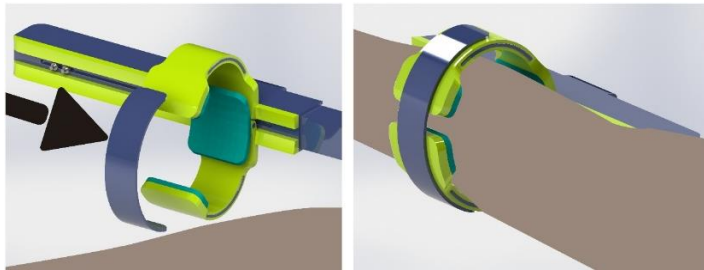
Mecanismo de Ajuste, Brazaletes MOVJOB, Fuente: Autor MOVJOB
